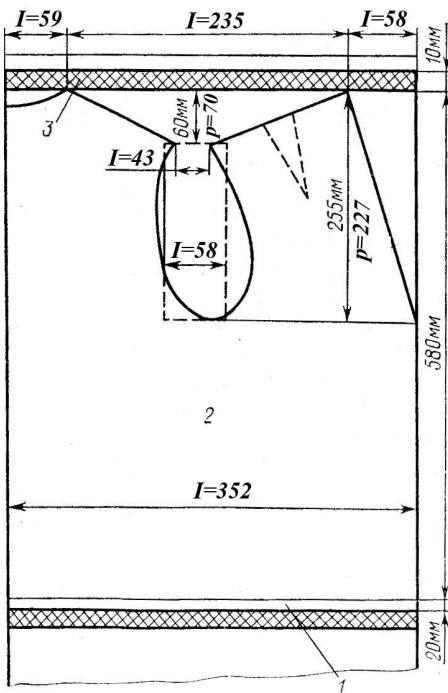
Робочі креслення купона стану Рис. 3.4 Робочі креслення купона рукавів стану
